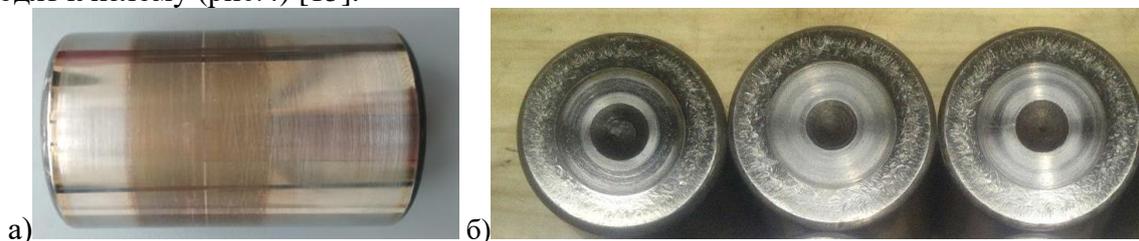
Детали подшипников с дефектами относящиеся к основным причинам отказов а-цвета побежалости б- ёлочка на телах качениях
